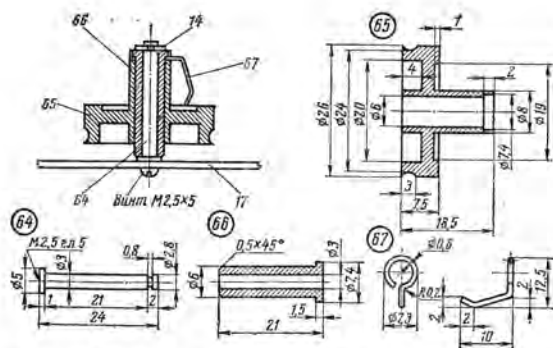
Подающий (приемный) узел: 14 — шайба установочная; 17 — шайба; 64 — ось, Ст. А12, 1 шт.; 65 — шкив подкатущечника, Д16-Т, 1 шт.; 66 — втулка, ЛС59-1, 1 шт., запрессовать в деталь 65; 67 — фиксатор, проволока стальная диаметром 0,6 мм, 1 шт.
